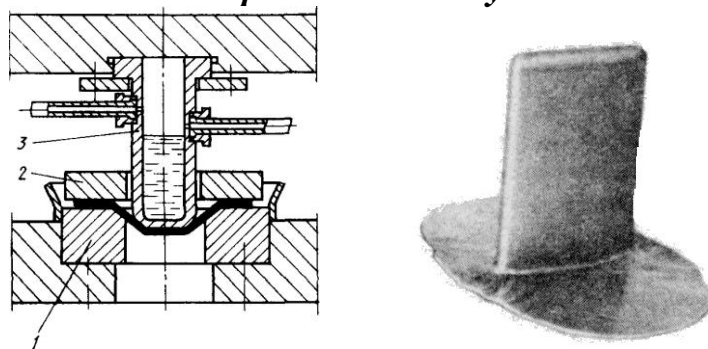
Схема штампа для вытяжки с глубоким охлаждением опасного сечения детали и Типовая деталь, полученная с использованием местного нагрева или холода: 1 — матрица, 2 — прижимное кольцо, 3 — пуансон
